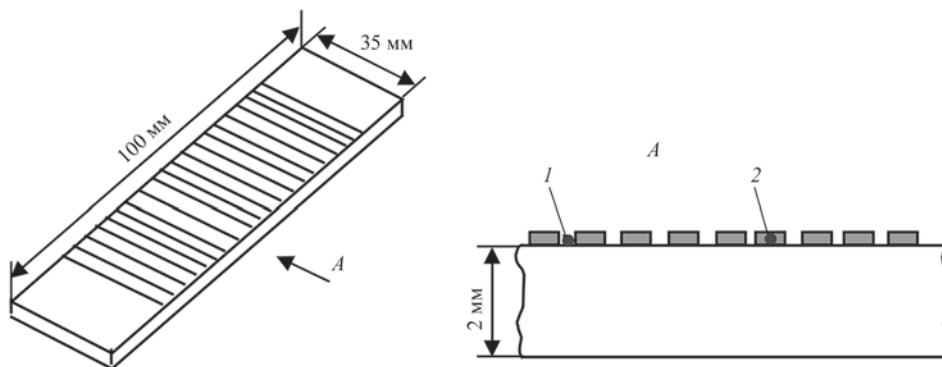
Пластина контрольного зразка типу I (схематично): 1 – поперечні тріщини, 2 – хромонікелеве покриття завтовшки 10, 20, 30, 50 мкм
